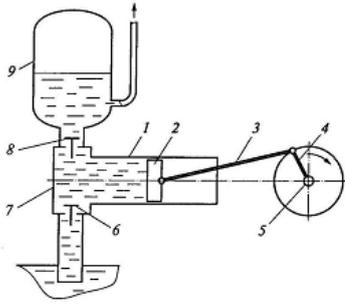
Поршневой насос простого действия: 1 – цилиндр; 2 – поршень; 3 – шатун; 4 – кривошип; 5 – вал; 6 – всасывающий клапан; 7 – клапанная коробка; 8 – напорный клапан; 9 – воздушный колпак.
